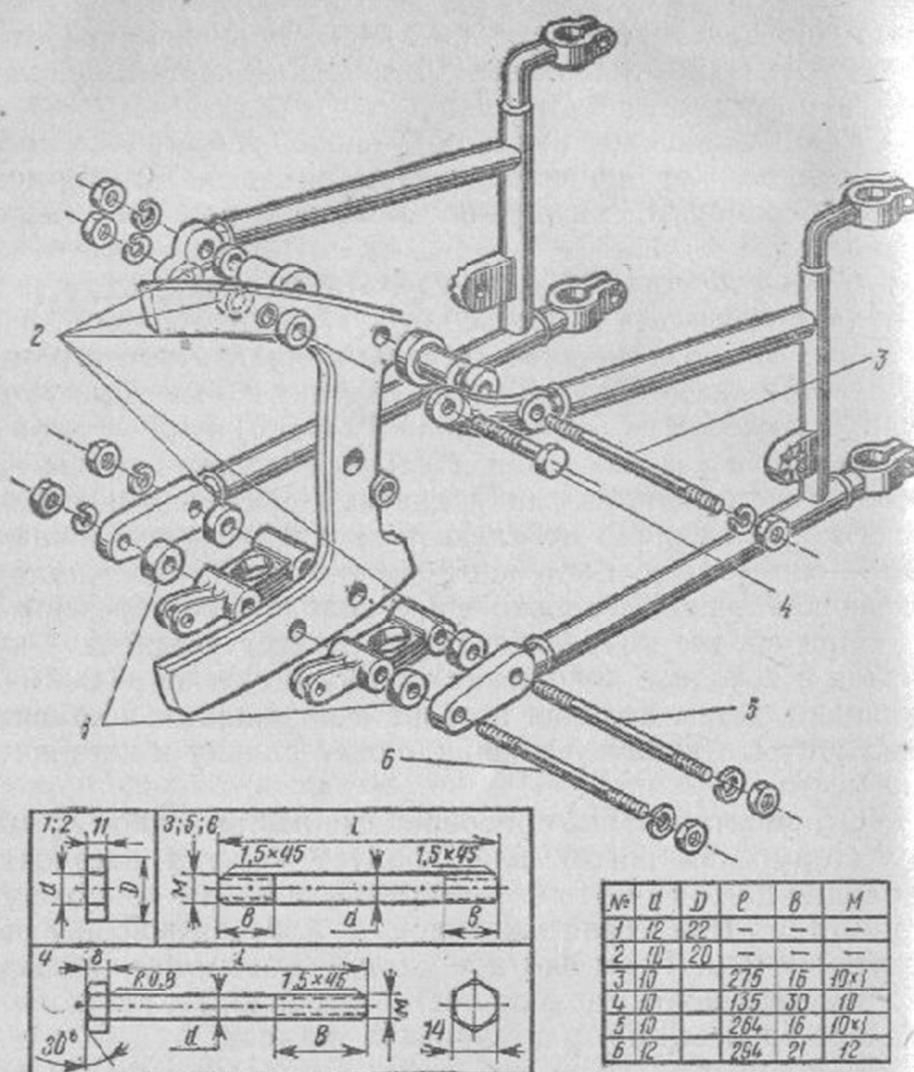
Переделка задней части рамы Иж-49 и нужные для этого детали:
